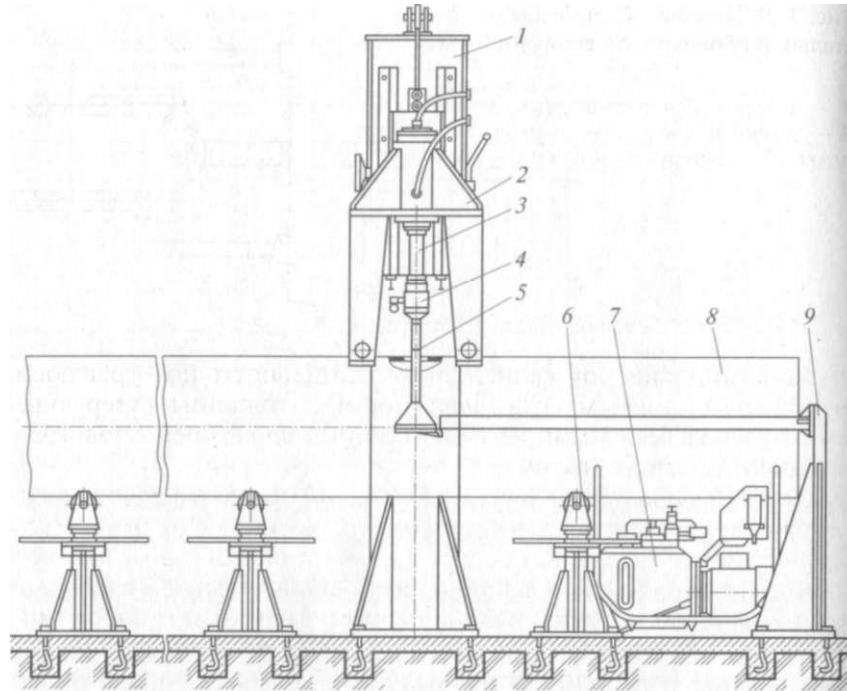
Установка для вытяжки ответвлений в трубах:
